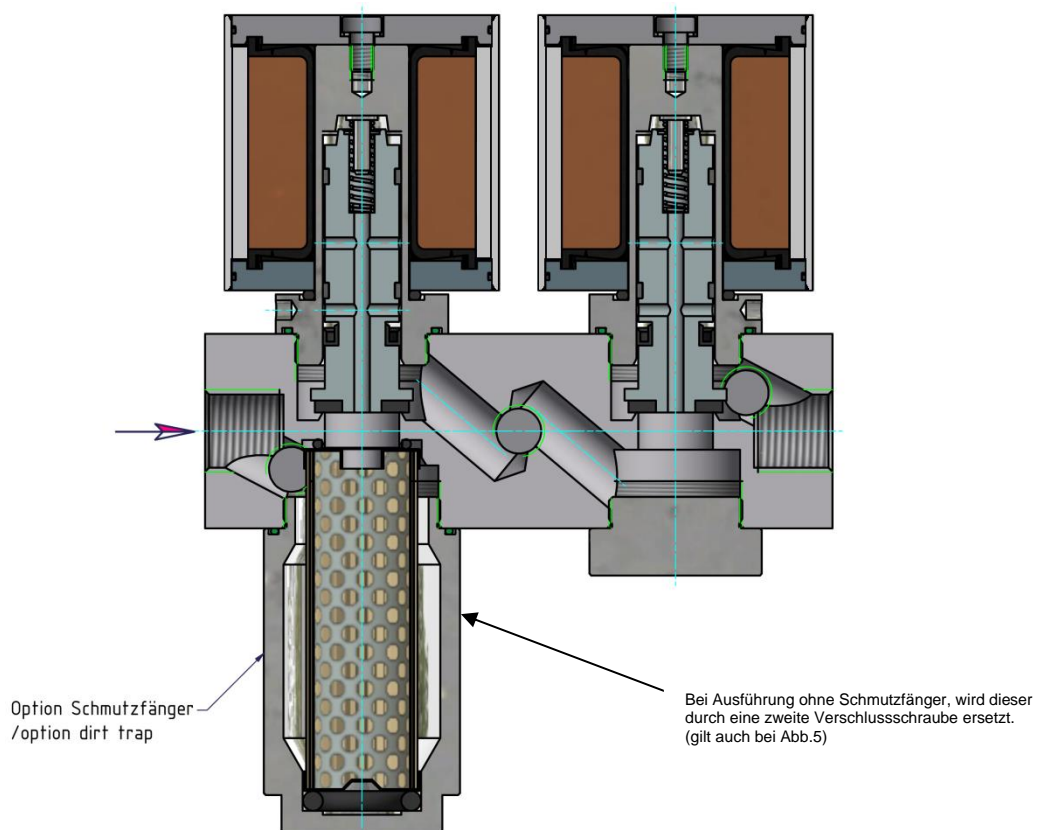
Flanschausführung VS...N.. mit Schmutzfänger (116.002.293)
